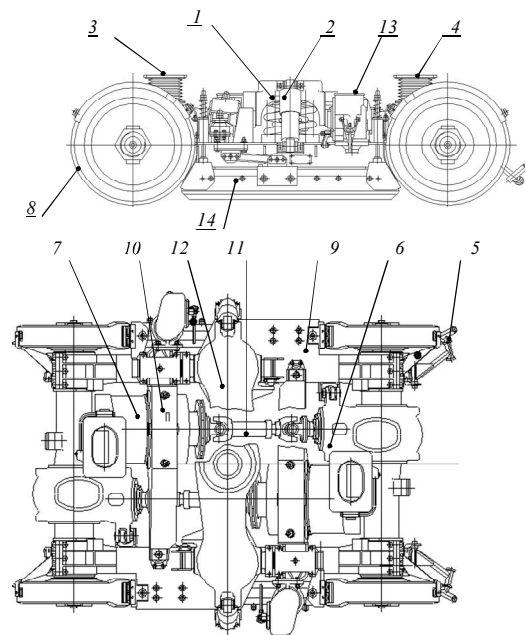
Візок трамвайного вагона «Спектр»: 1 - циліндрична пружина; 2 - гідравлічний гаситель коливань; 3 - вентиляційний кожух; 4 - крила; 5 - патрубок пісочниці; 6 - редуктор; 7 - тяговий двигун; 8 - колесо; 9 - поздовжня балка; 10 - поперечна балка; 11 - карданний вал; 12 - надресорная балка; 13 - електромагнітний привід рейкового гальма; 14 рейковий гальмо
